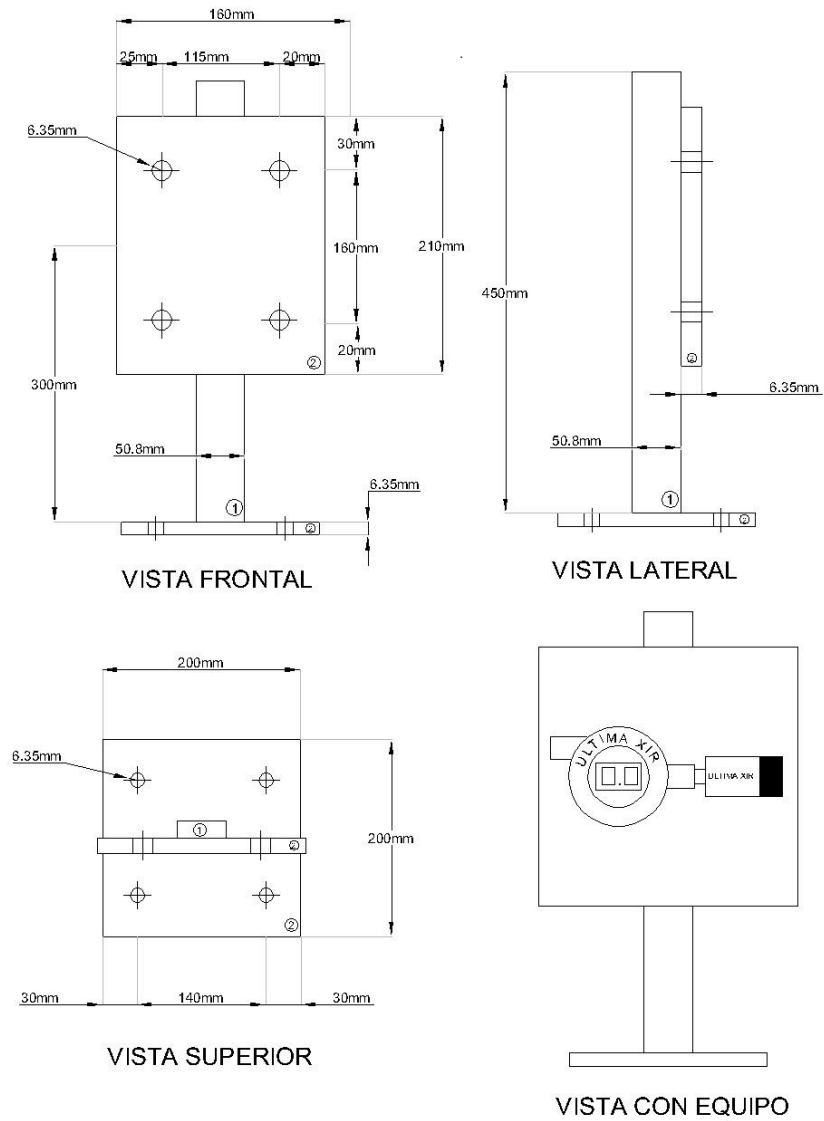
Diseño para llenaderas de Autotanque y Patines de Medición.
